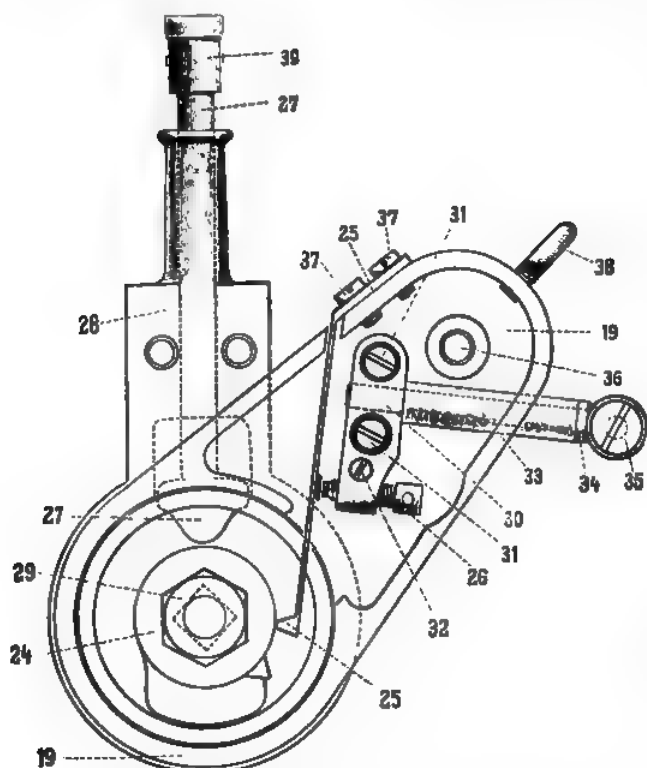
Einstellbarer Unterbrecher des Z. L.-Motors.
